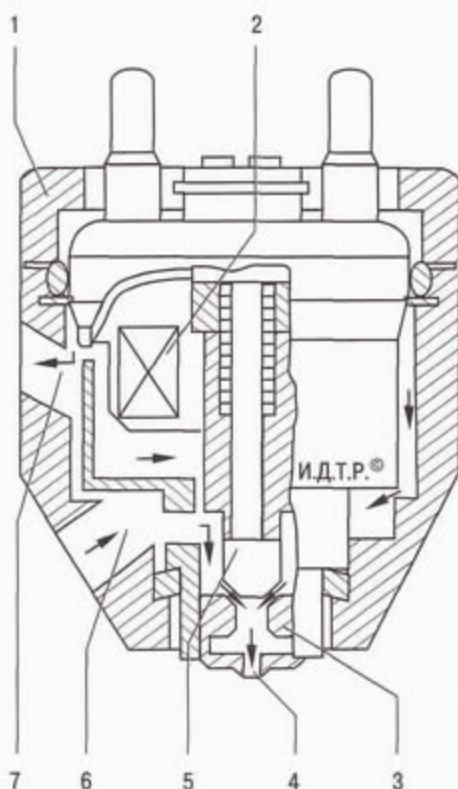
Форсунка: 1 – корпус форсунки; 2 – электромагнит; 3 – седло клапана; 4 – сопло; 5 – плунжер; 6 – канал подвода топлива; 7 – канал слива топлива
